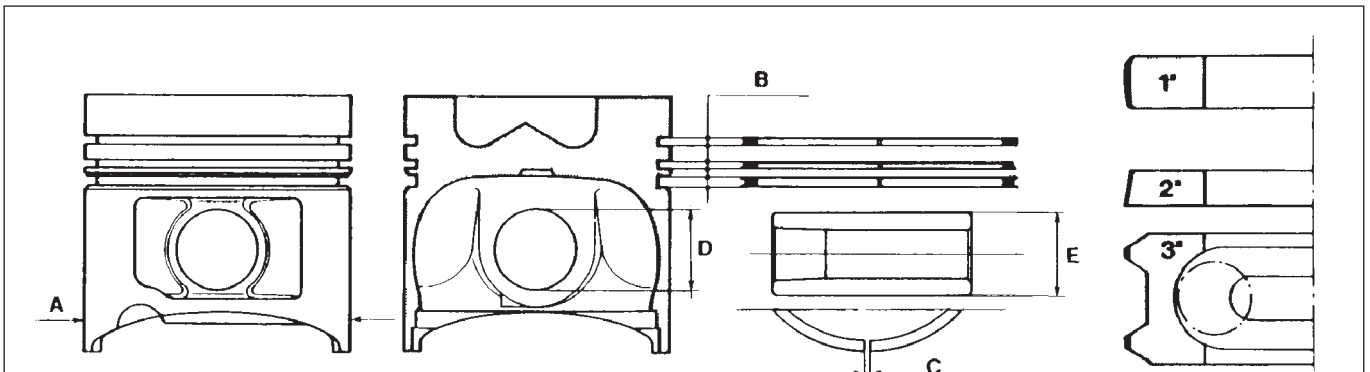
Maßigenschaften von Kolben, Kolbenringen und Kolbenbolzen.
